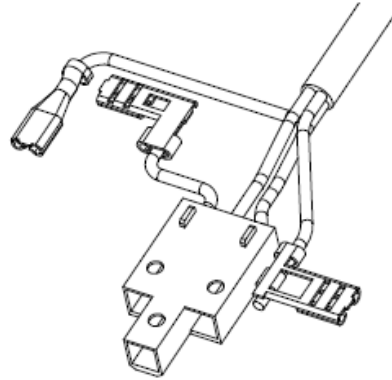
Cabo do motor dos compressores da série VNE com OLP
